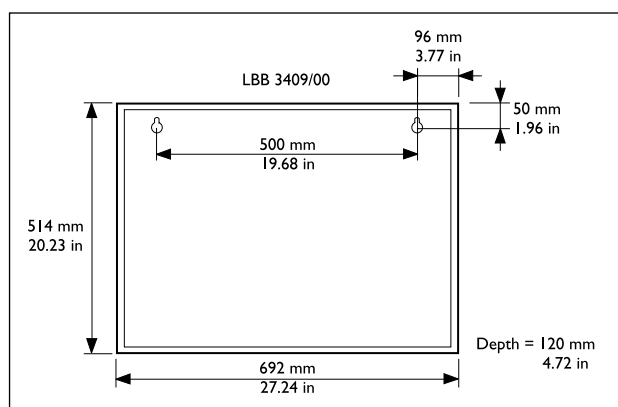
Dimensioni di montaggio della postazione di ricarica
